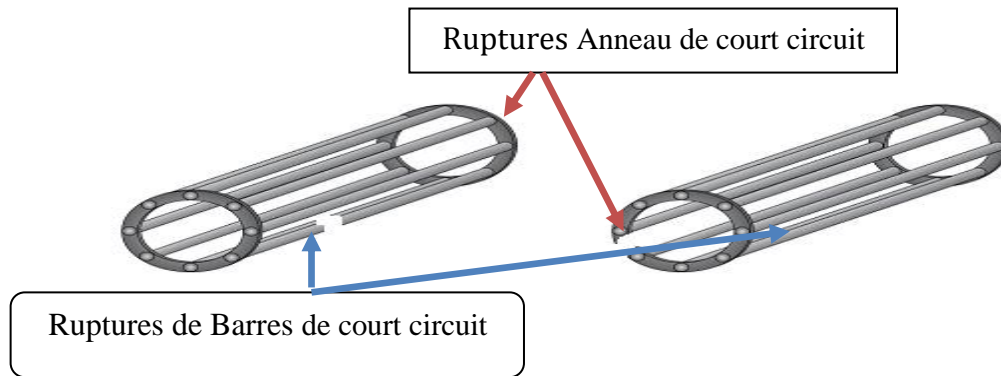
Défaut d'un rotor à cage d'écureuil.
